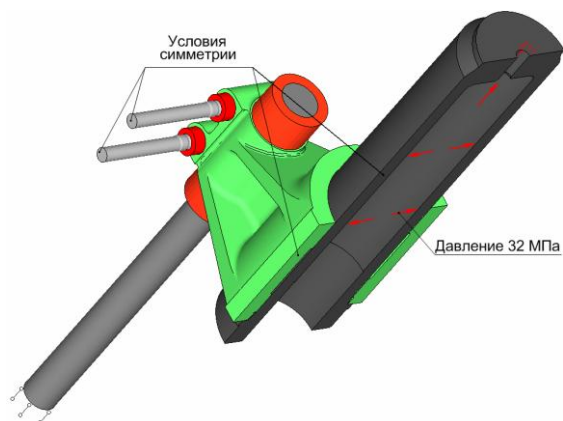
Расчетная схема станины и цилиндра прошивного устройства
